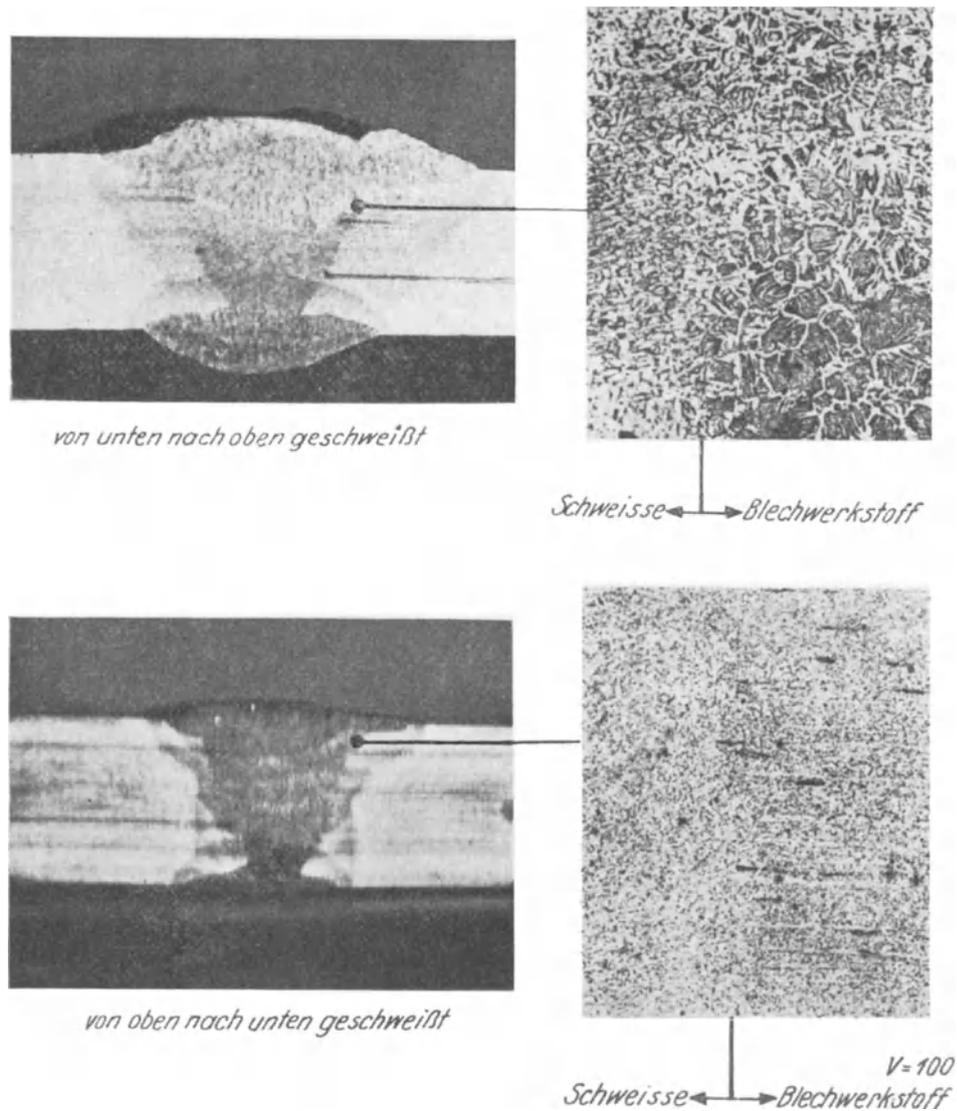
Gefügebilder der Querschnitte von Senkrecht-Nähten mit leicht ummantelter Elektrode von unten nach oben und von oben nach unten geschweißt.
